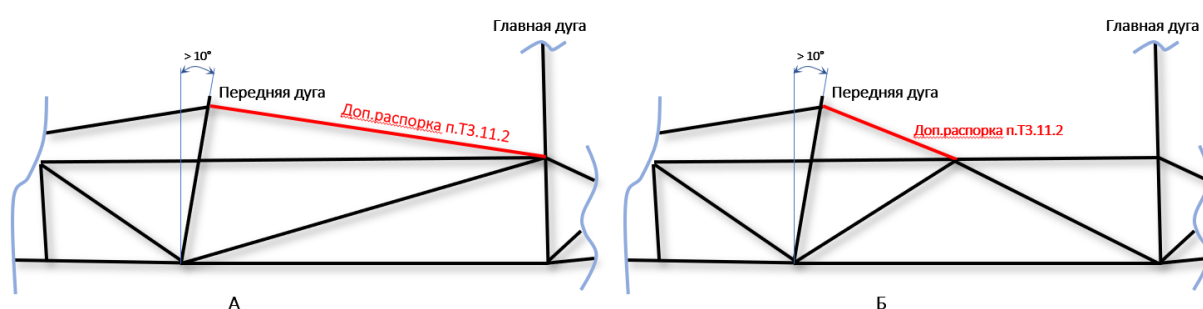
Схема расположения дополнительных распорок передней дуги
